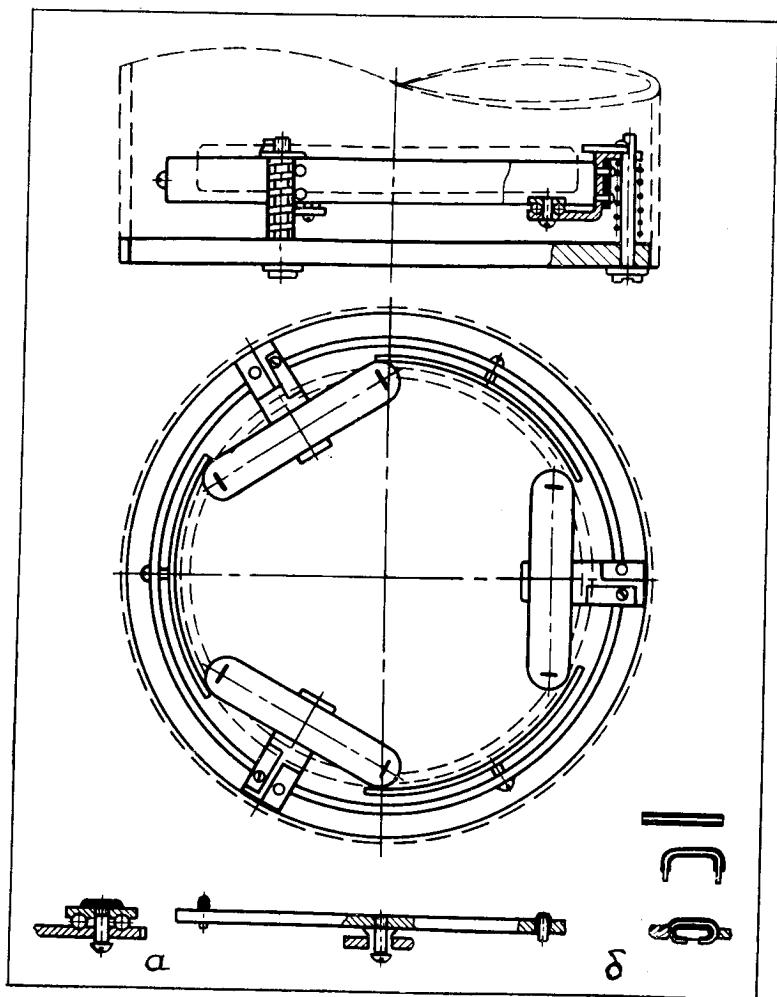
Конструкция оправы для зеркала больших размеров:
